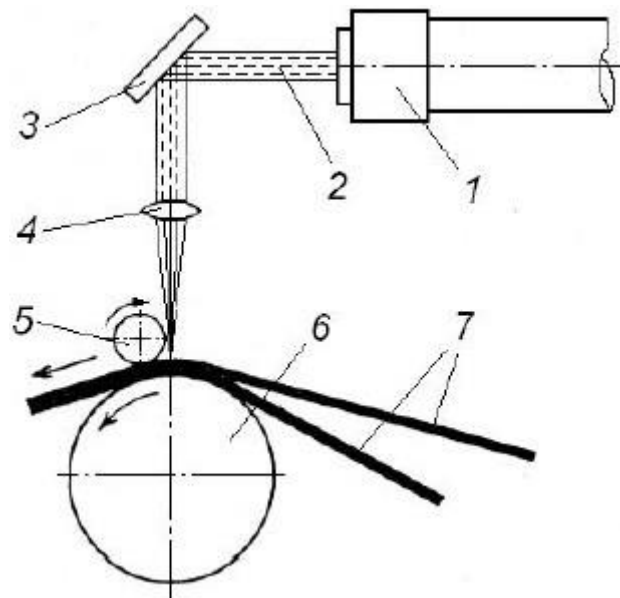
Схема сварки пленки лучом лазера: 1 – лазер; 2 – луч; 3 – отклоняющее зеркало; 4 – фокусирующая линза; 5 – прикатывающий ролик; 6 – транспортирующий ролик; 7 – свариваемые пленки
